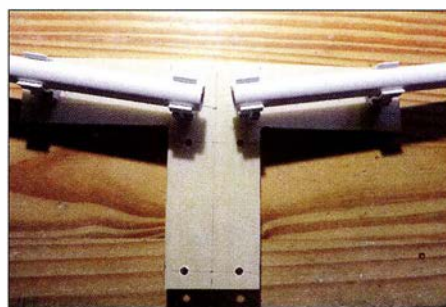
Trägerplatte mit montierten Klemmschellen und Installationsrohren
